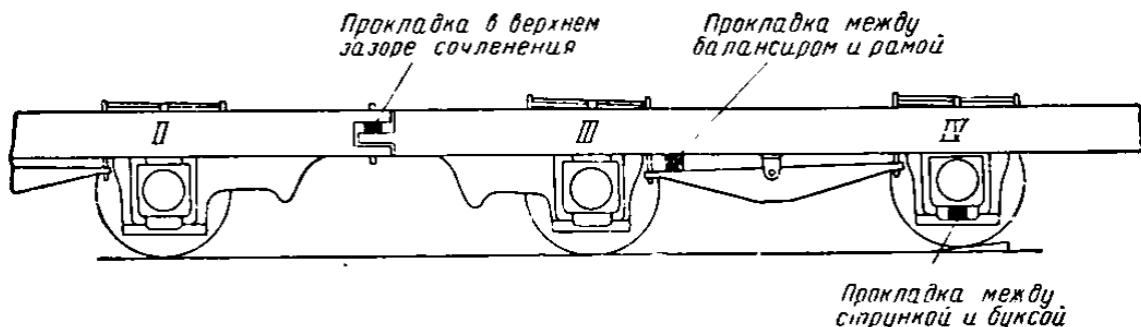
Расположение приспособлений при вывешивании четвертой колесной пары
